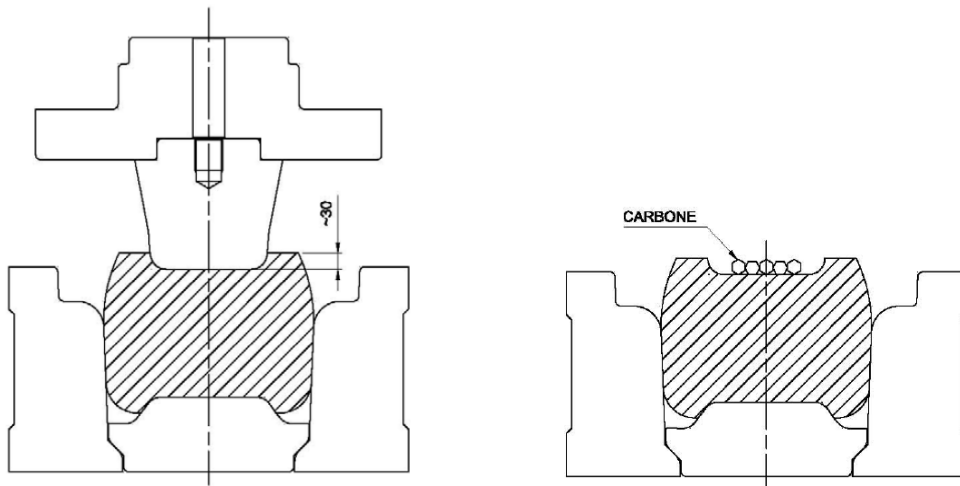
Improntatura della billetta per l' inserimento di granelli di carbone.
